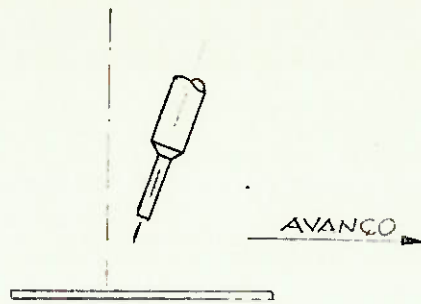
POSIÇÃO DO ELÉTRODO NA SOLDAGEM PLANA
